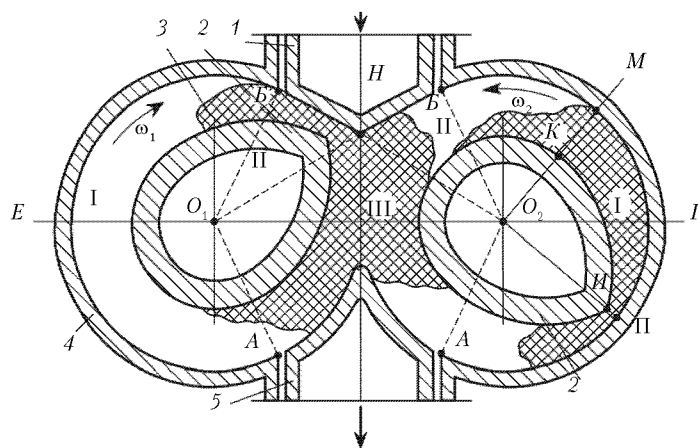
Схема двухроторного смесителя закрытого типа: 1 и 5 — верхний и нижний затворы; 2 — роторы; 3 — композиция; 4 — камера смесителя; I, II, III — зоны перемешивания
